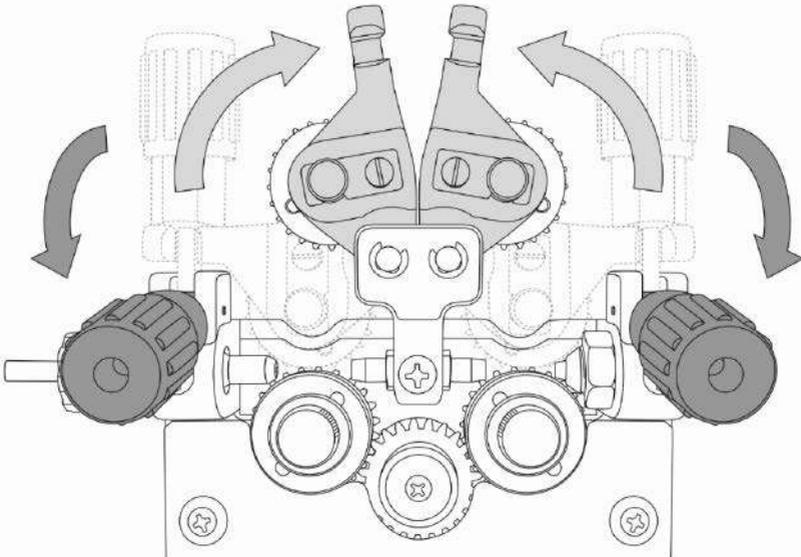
Подготовка сварочной проволоки.
